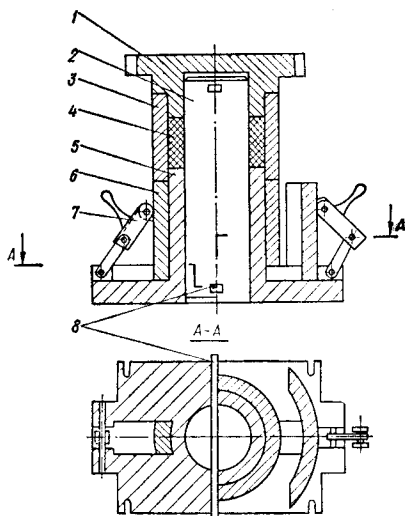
Конструктивное оформление пресс-формы для изделий типа «Цилиндр».
